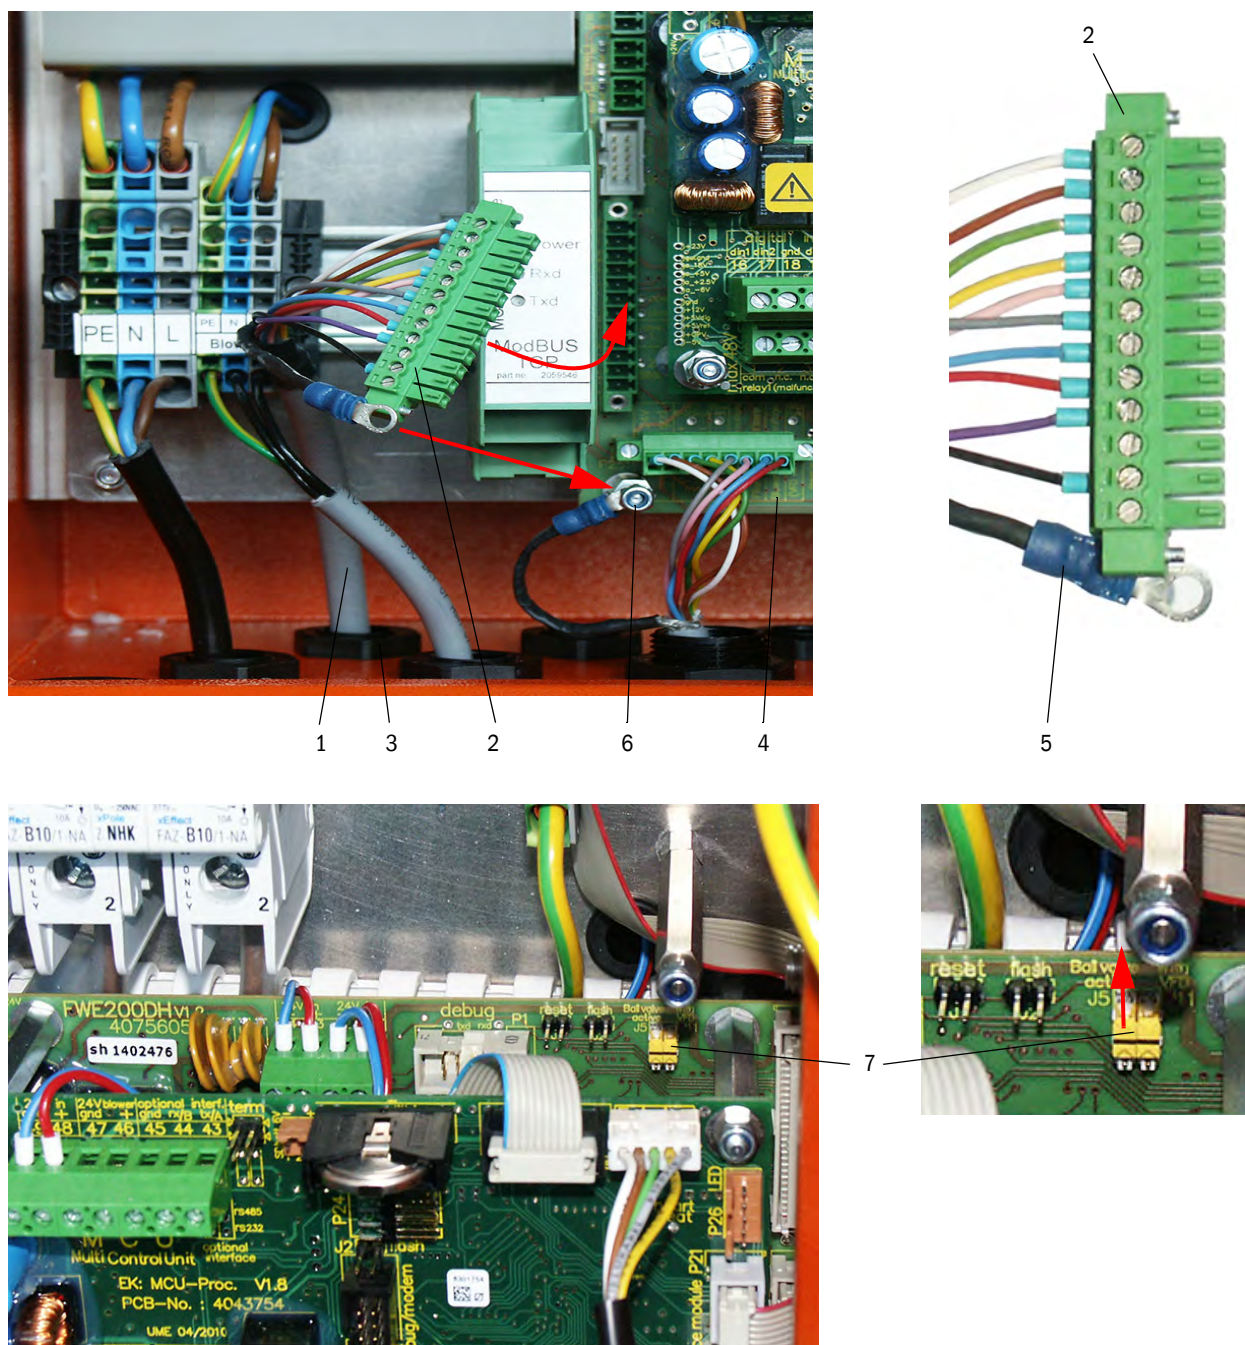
Montaggio del sottogruppo di retrolavaggio sull'unità di misura e controllo
